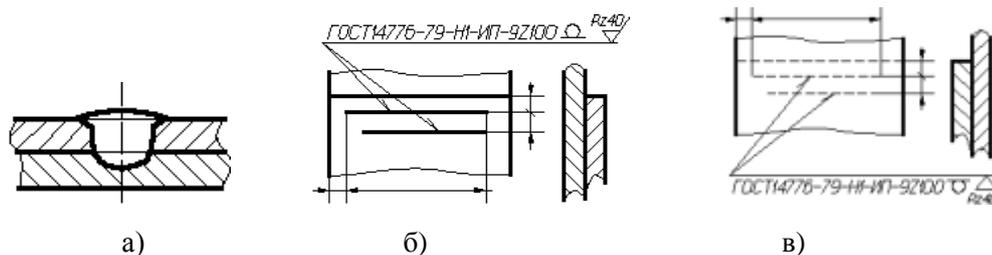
Шов точечный соединения внахлестку: а) форма поперечного сечения шва; б) с лицевой стороны; в) с оборотной стороны
